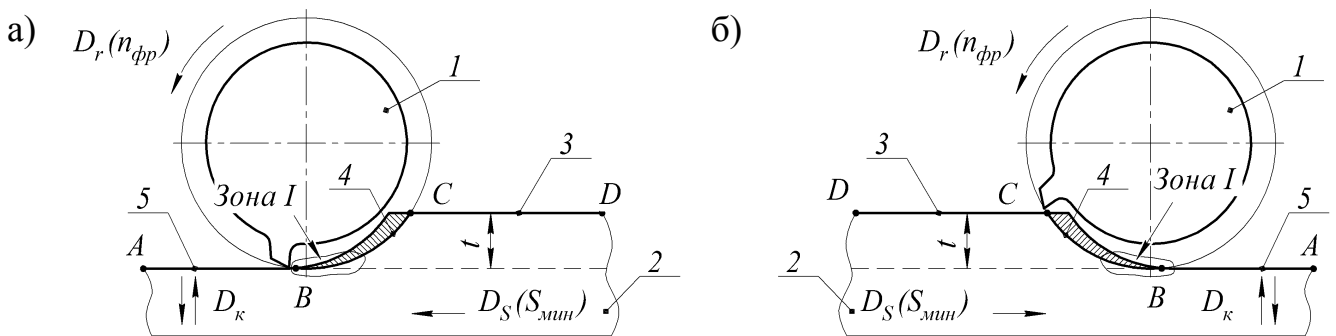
Схема циліндричного фрезерування тонкостінної деталі:
